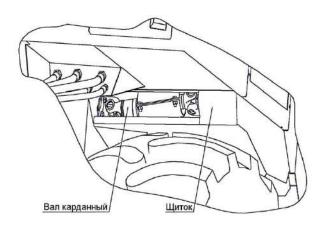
Смазка шарниров карданного вала привода редуктора гидронасосов
